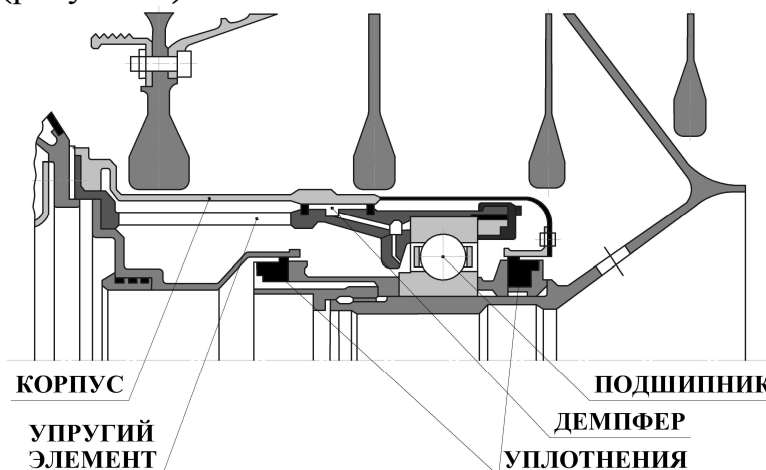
Передняя опора компрессора высокого давления двигателя Д-36
